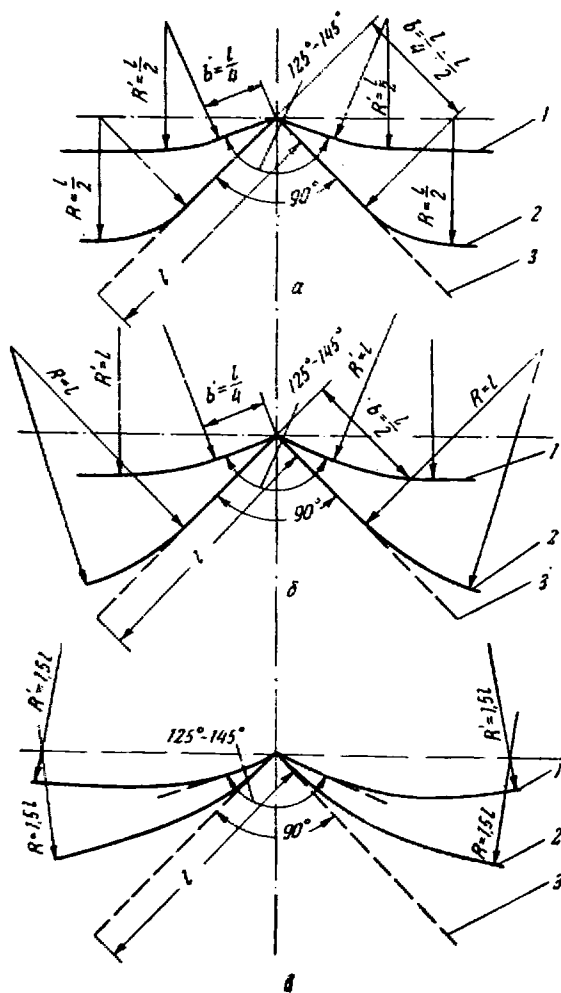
Способы построения калибров угловой стали с развернутыми полками
